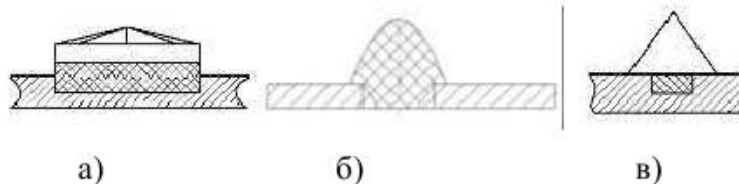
Шипы: а – приварка контактной сваркой диска с одновременным формированием поверхности трения; б – наплавка в аргоне; в – приварка контактной сваркой, конической заготовки; двойной штриховкой показана область расплавления металла
